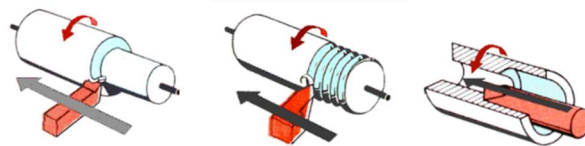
Algumas operações de torneamento, roscagem exterior e torneamento interior (Moldes, 2020)
